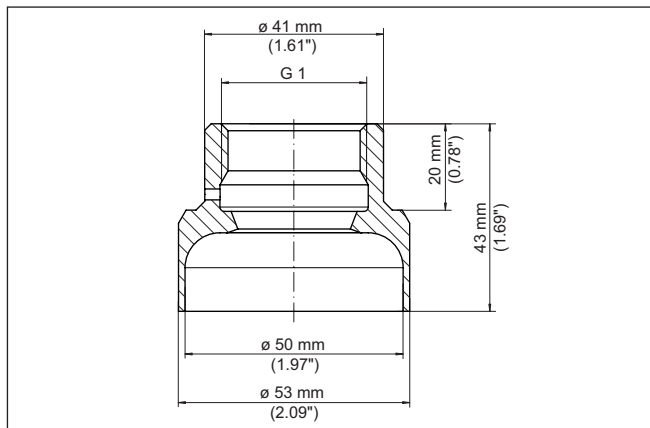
Dimensions raccord à souder direct pour montage sur tube G1 (ISO 228-1) - joint conique
